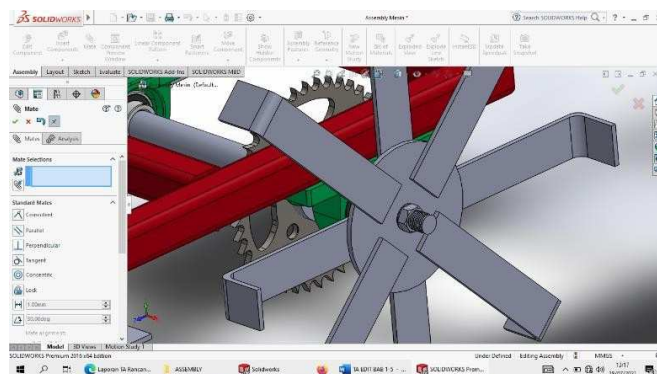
157 Hasil *Assembly Bolt* dan Poros Roda
